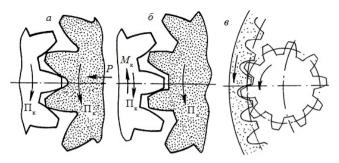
Методы шлифования профиля зубьев цилиндрических колес
